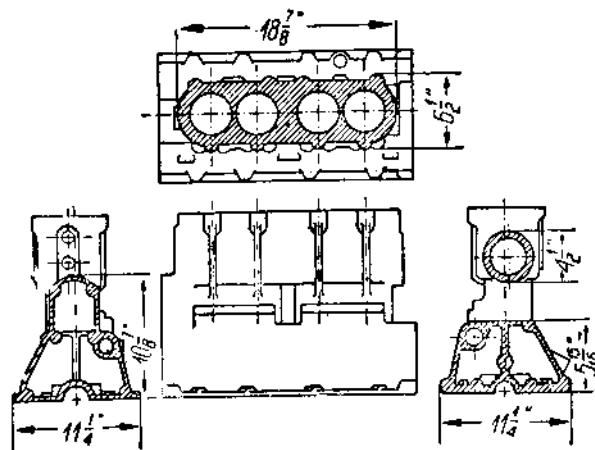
Блок, обработанный на станке Ингерсоль (по рис. 305). Места обработки заштрихованы.
